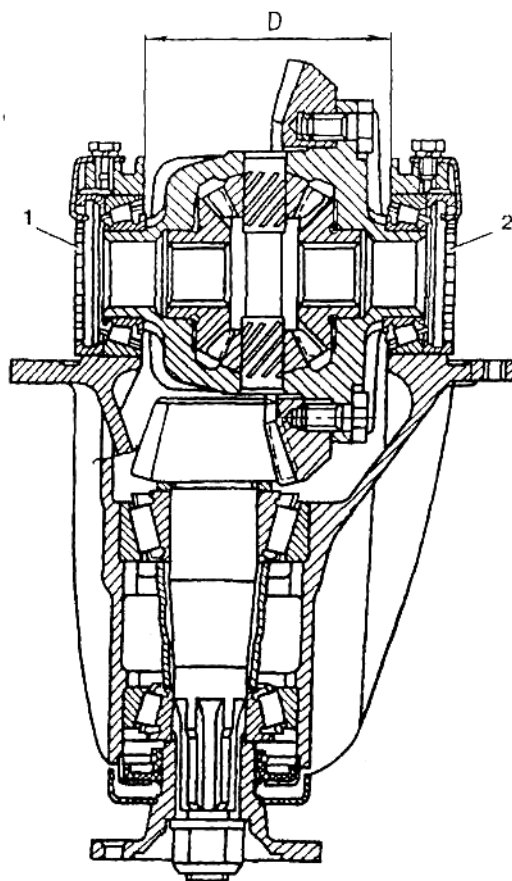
Схема проверки предварительного натяга подшипников коробки дифференциала:
